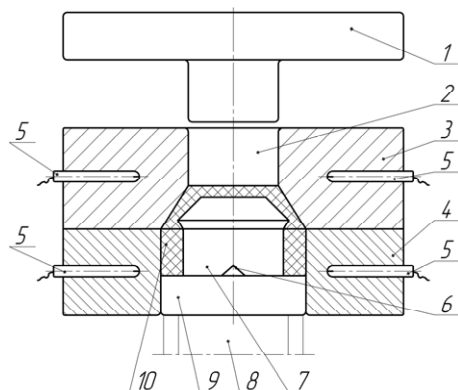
Схема восстановления детали на прессовке: 1 – пуансон; 2 – загрузочная камера; 3, 4 – верхняя и нижняя части пресс-формы; 5 – термоэлектрические нагреватели; 6 – установочный выступ; 7 – восстанавливаемая деталь; 8 – выталкиватель; 9 – опорная плита; 10 – наращиваемый слой
